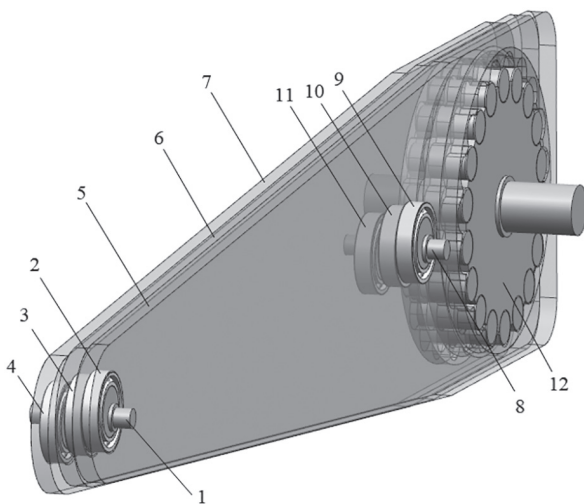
Компьютерная модель эксцентриковой передачи с ведущим и дополнительным эксцентриковыми валами (первый вариант передачи)
